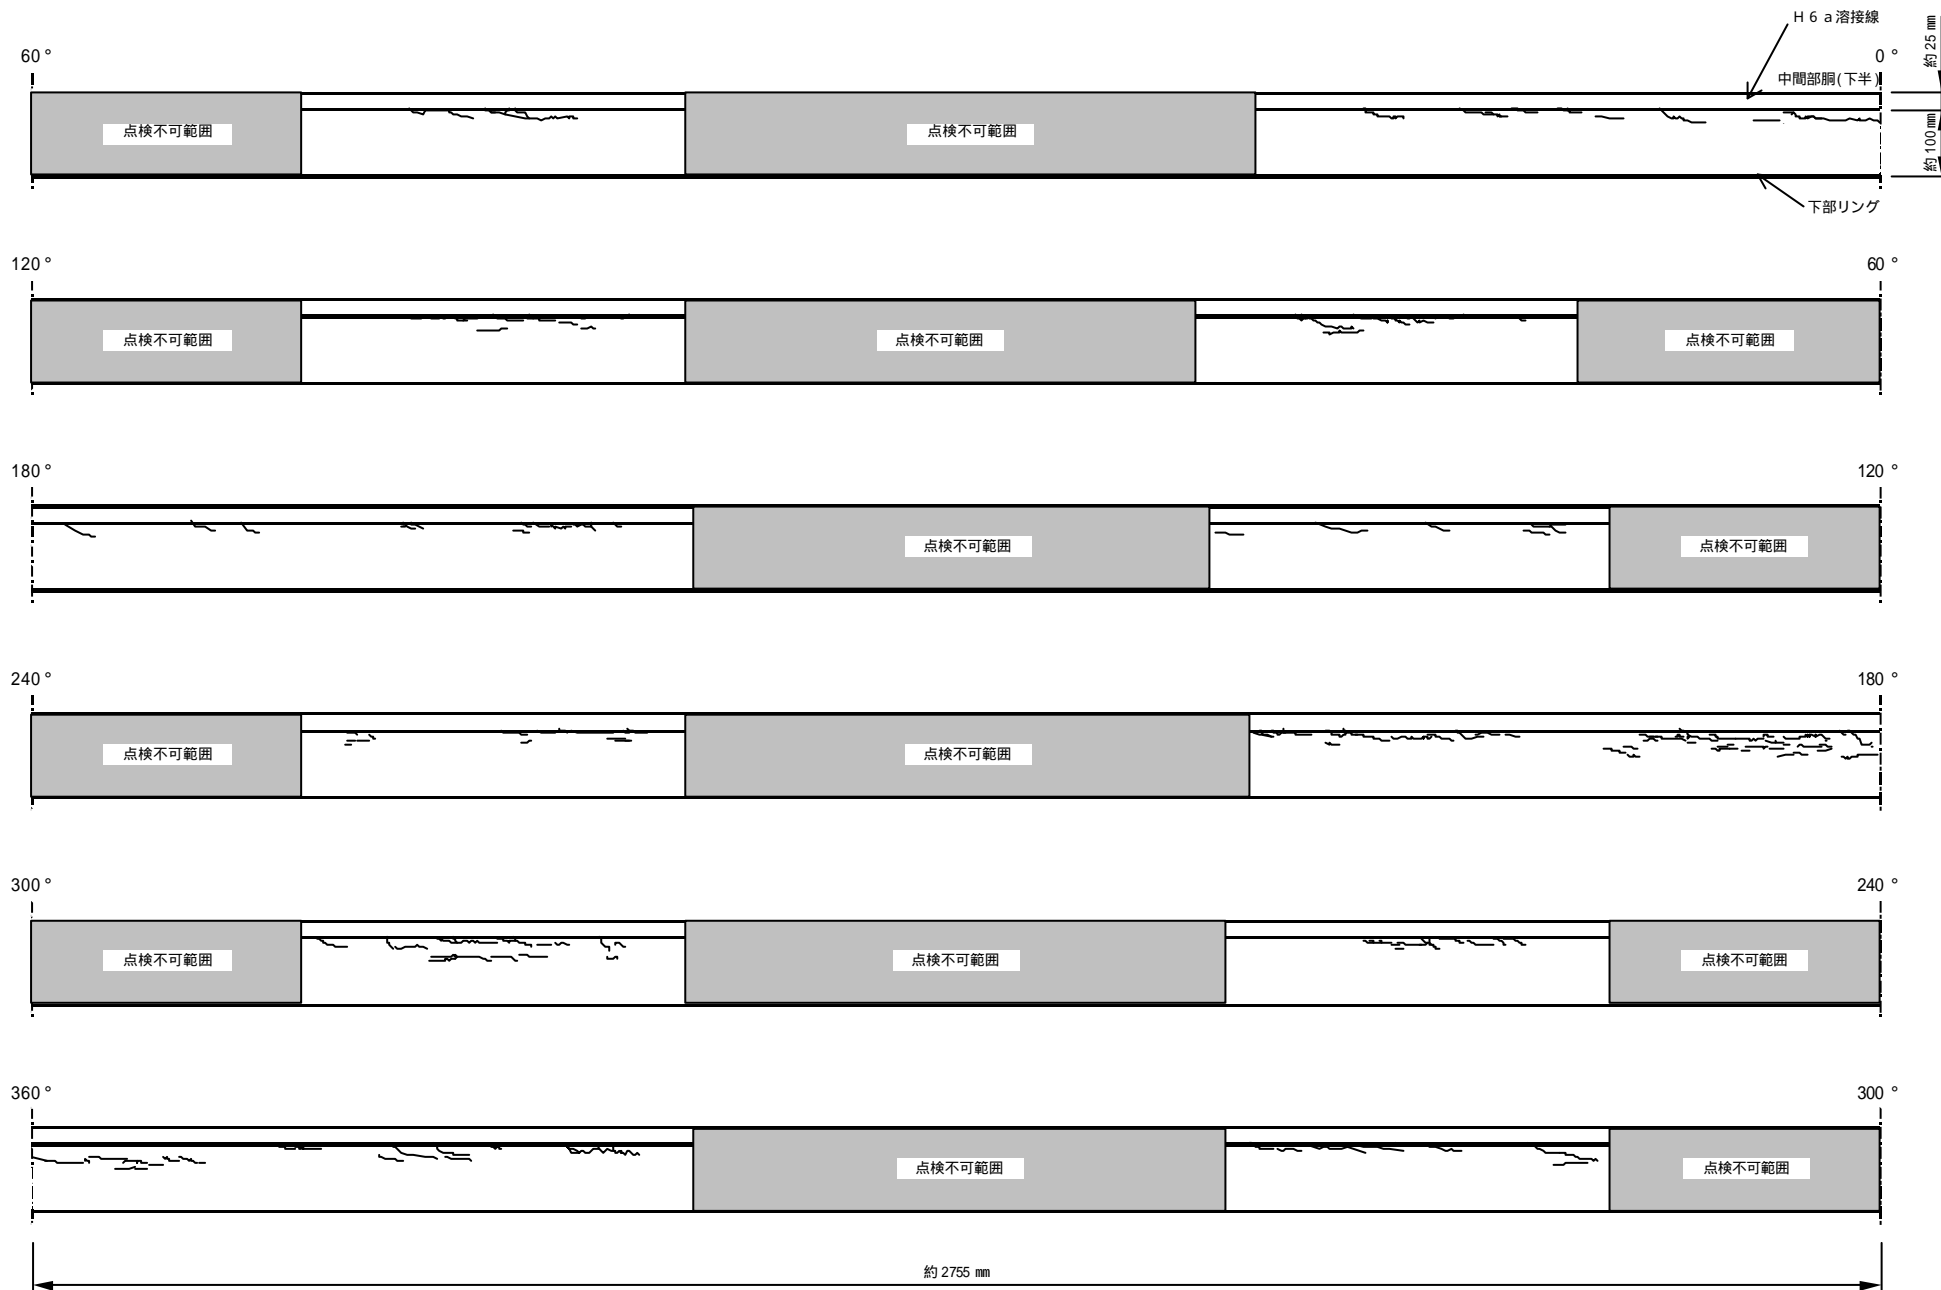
：シュラウド下部リング外側溶接線（H6a 外）付近目視点検結果
